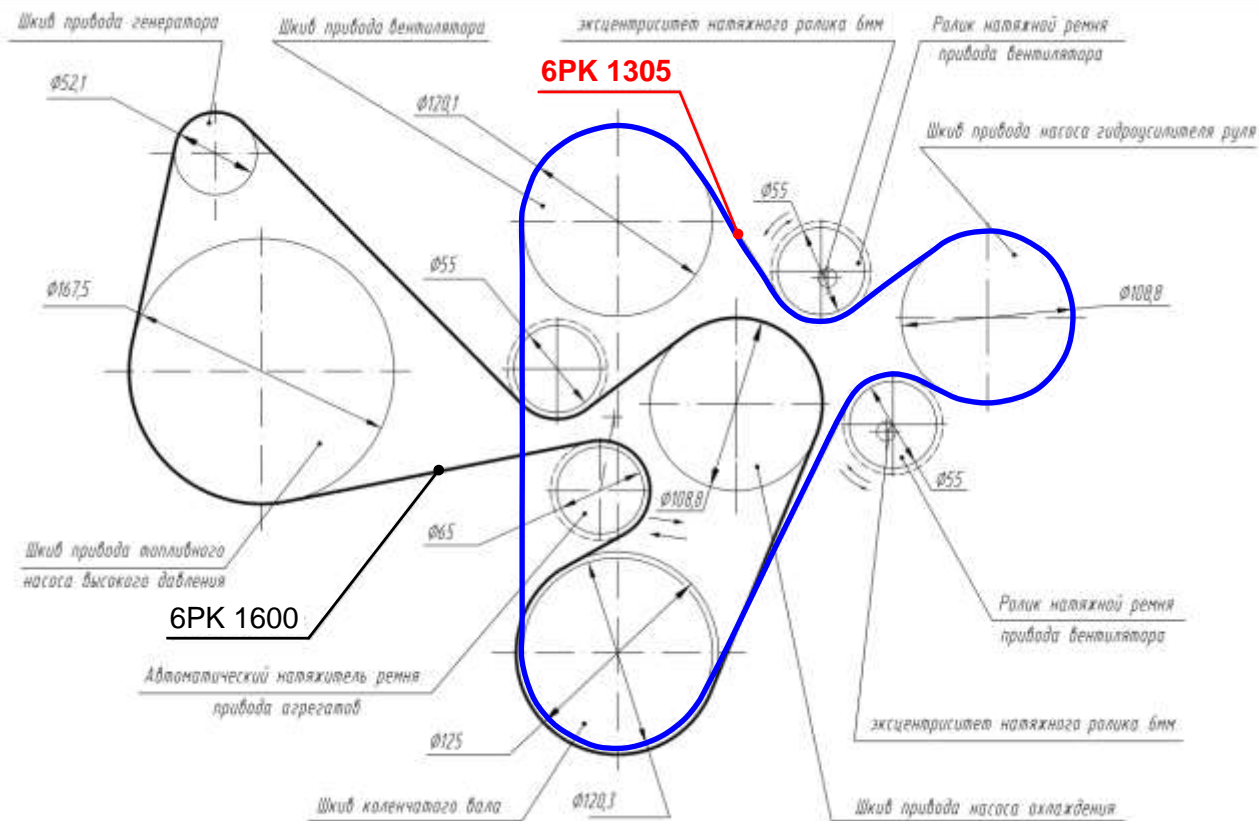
Схема привода вспомогательных агрегатов двигателя для автомобилей на платформе УАЗ-315148.
